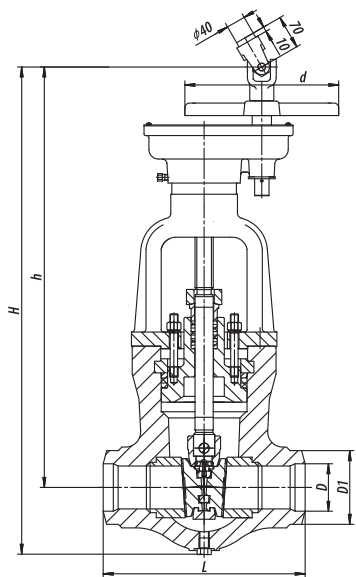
Задвижка DN100 с цилиндрическим редуктором
